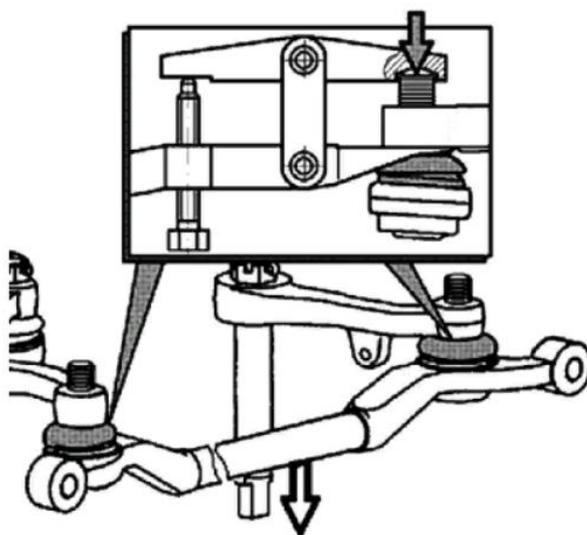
Внешний вид универсального съемника для выпрессовки шаровых пальцев
